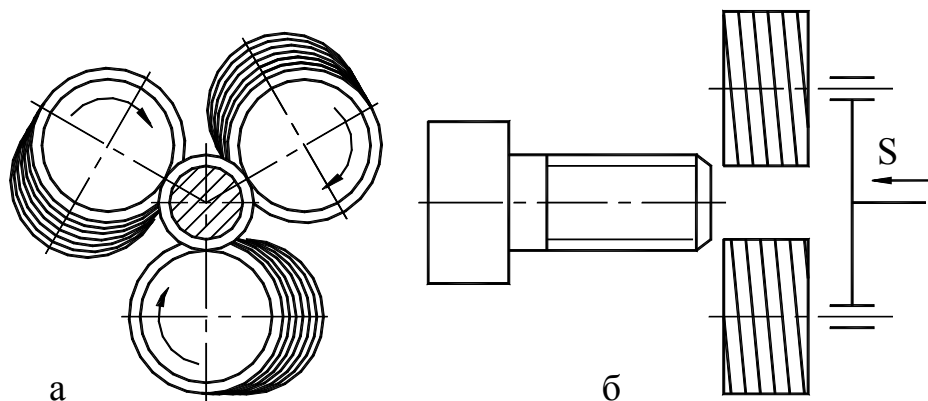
Схема накатки наружной резьбы резьбонакатными головками
